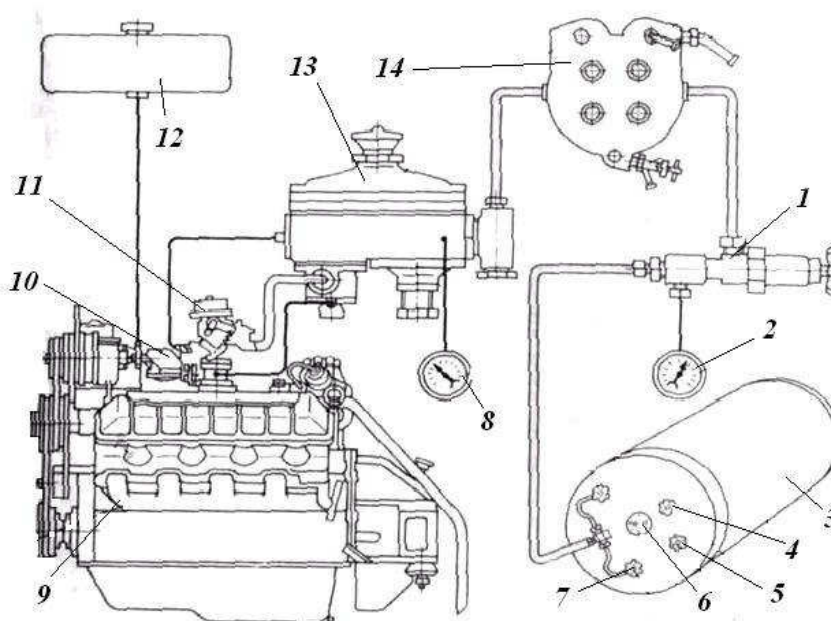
Схема газобаллонной установки для сжиженного газа: 1 - магистральный вентиль; 2 - манометр баллона; 3 - баллон для сжиженного газа; 4 - контрольный вентиль; 5 - наполнительный вентиль баллона; 6 - указатель уровня сжиженного газа; 7 - жидкостный вентиль; 8 - манометр редуктора; 9 - двигатель; 10 - карбюратор; 11 - смеситель газа; 12 - бак для бензина; 13 - газовый редуктор; 14 - испаритель сжиженного газа
